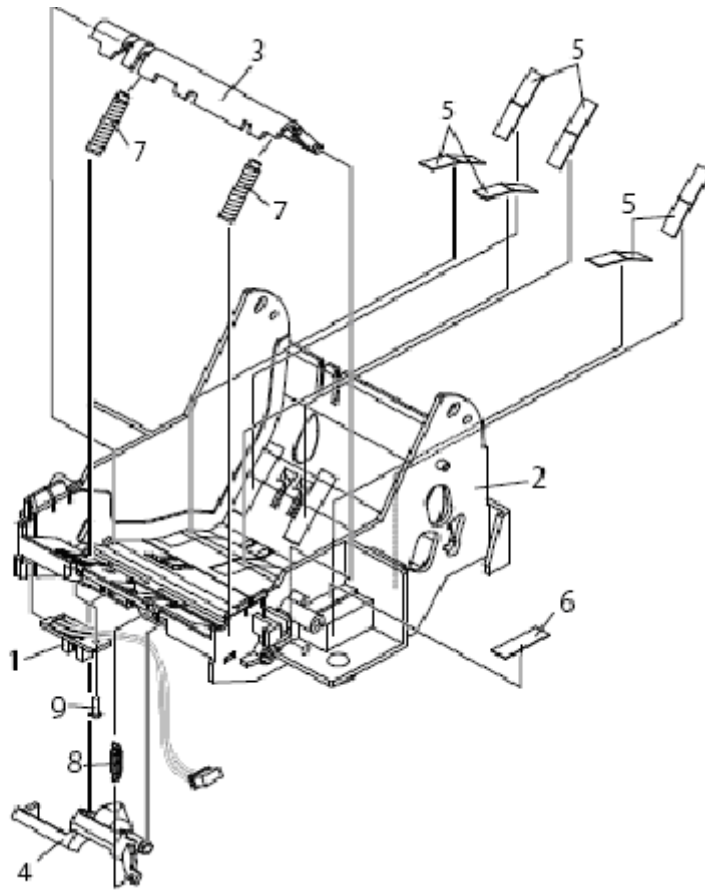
Схема полной разборки крышки чекового отсека
